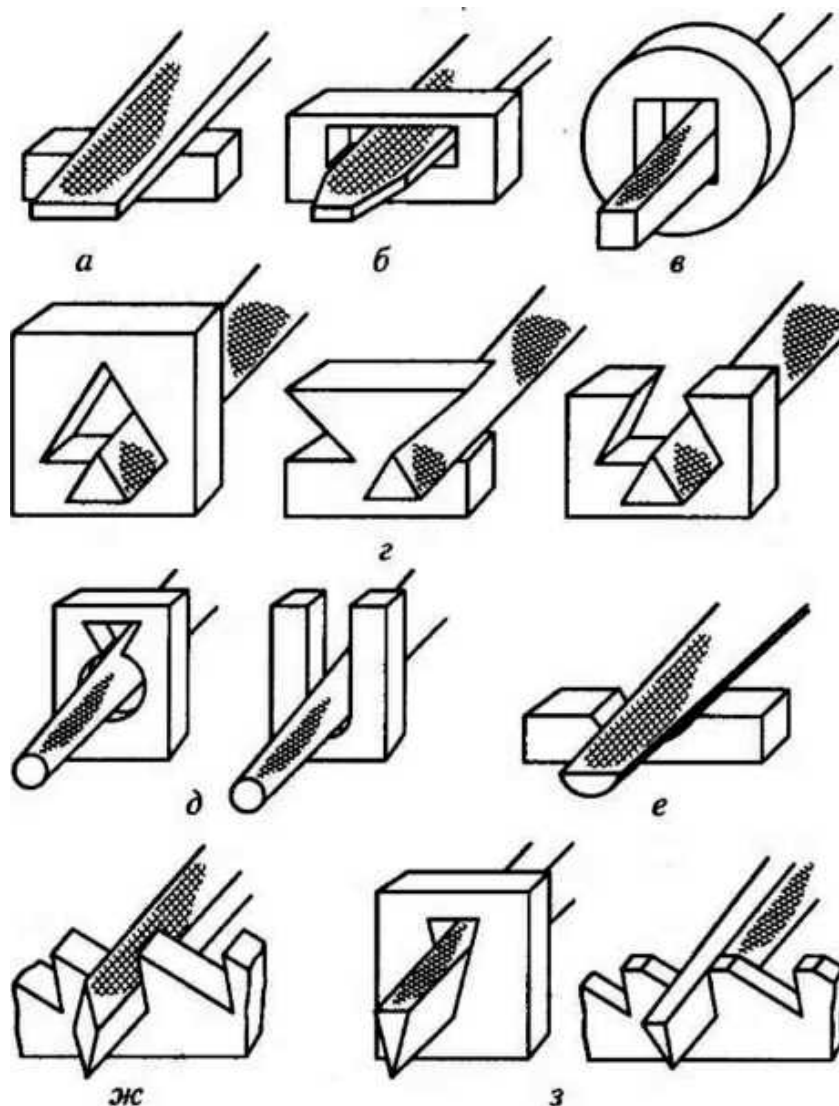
Формы поперечного сечения напильников и обрабатываемых поверхностей:
